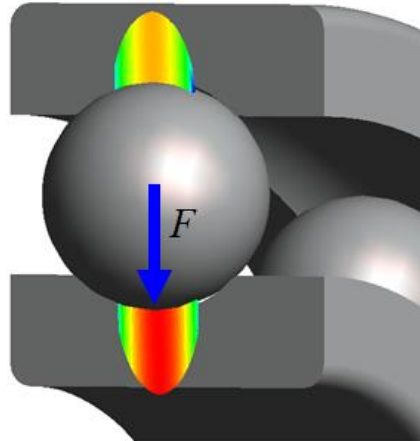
Aplicação de no rolamento durante a sua aplicação (Schaeffler KG 2009).
